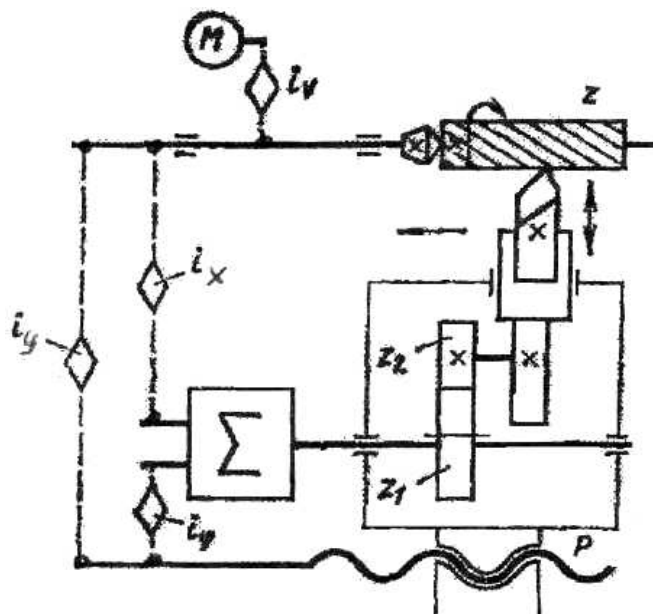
Структурная схема станка для затылования цилиндрических фрез со спиральными стружечными канавками
